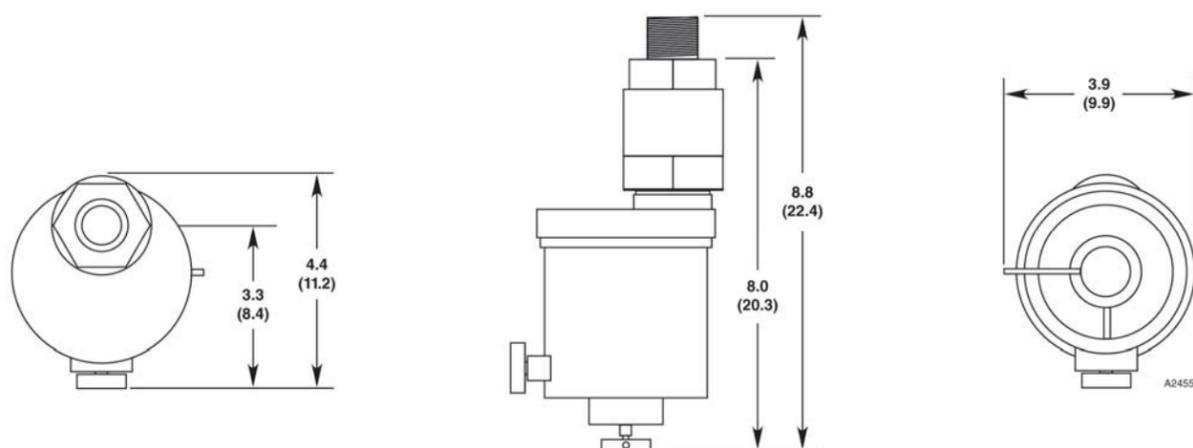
Габаритные размеры газоанализатора NTMOS с ампульным калибровочным набором и установленной смесительной камерой в дюймах (см).
